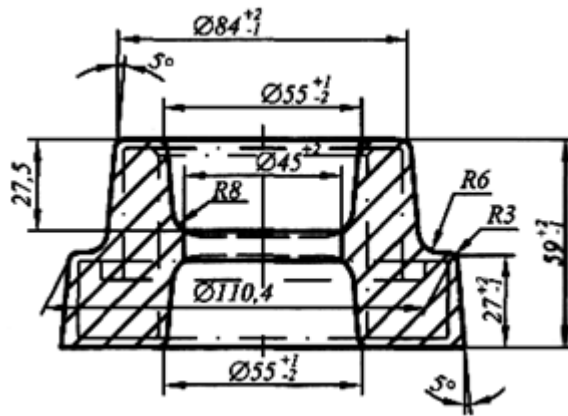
Чертёж молотовой штамповки в закрытом штампе.
